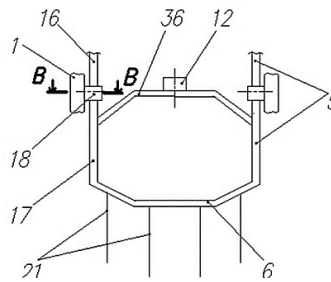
Установка вибратора на траверсу, соединяющую неподвижно нижние рычаги стоек подрезающей скобы корчевателя
